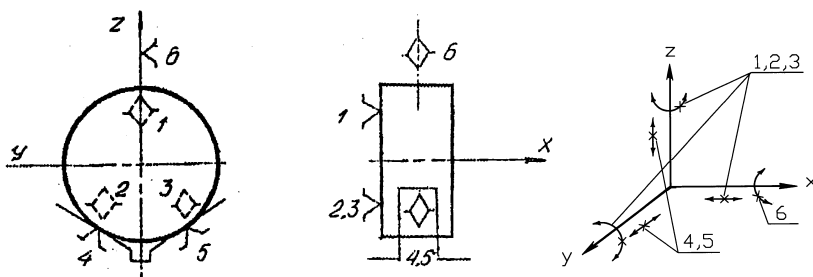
Теоретическая схема базирования заготовки типа диска по плоской и наружной цилиндрической поверхностям
